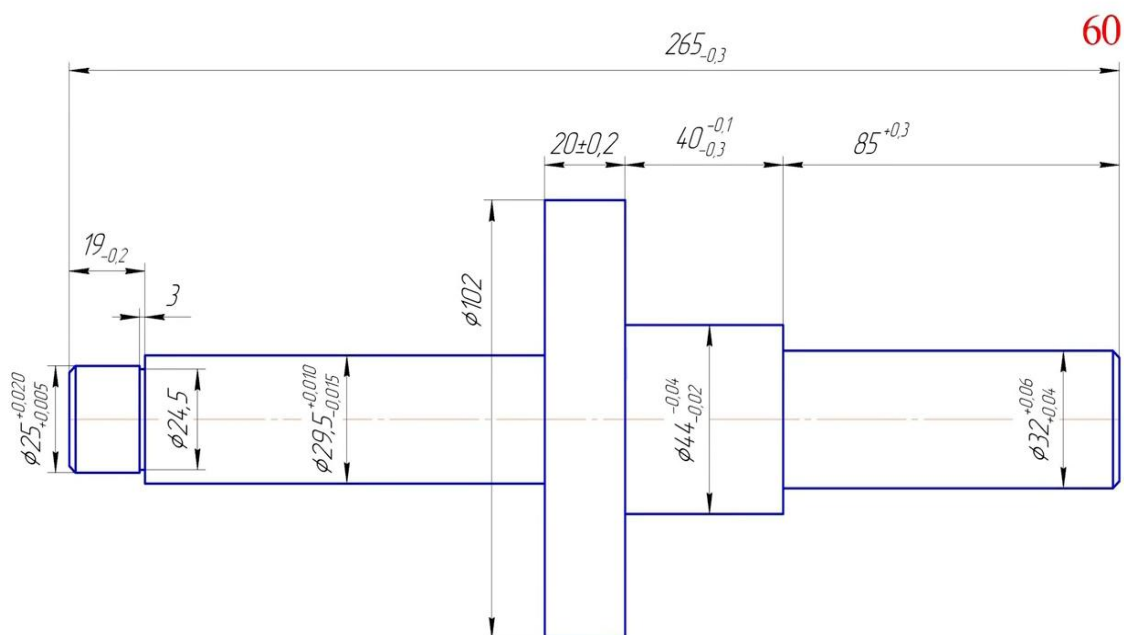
Примеры обозначений допусков на изготовление детали
